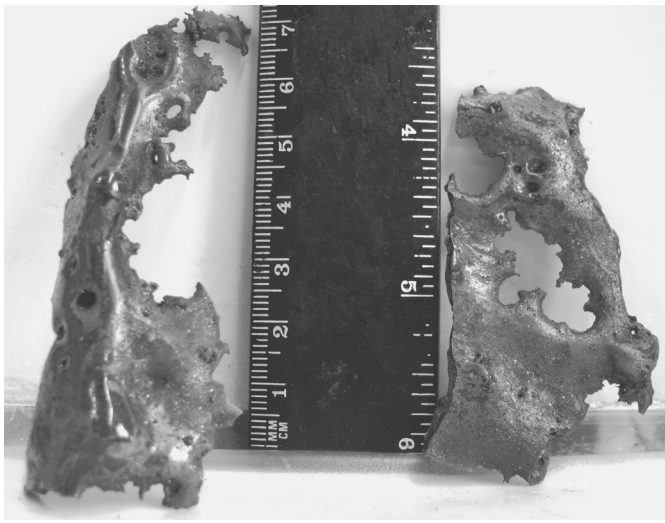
Фрагменты шлаковой корки подменисковой зоны с нарушением целостности поверхности
